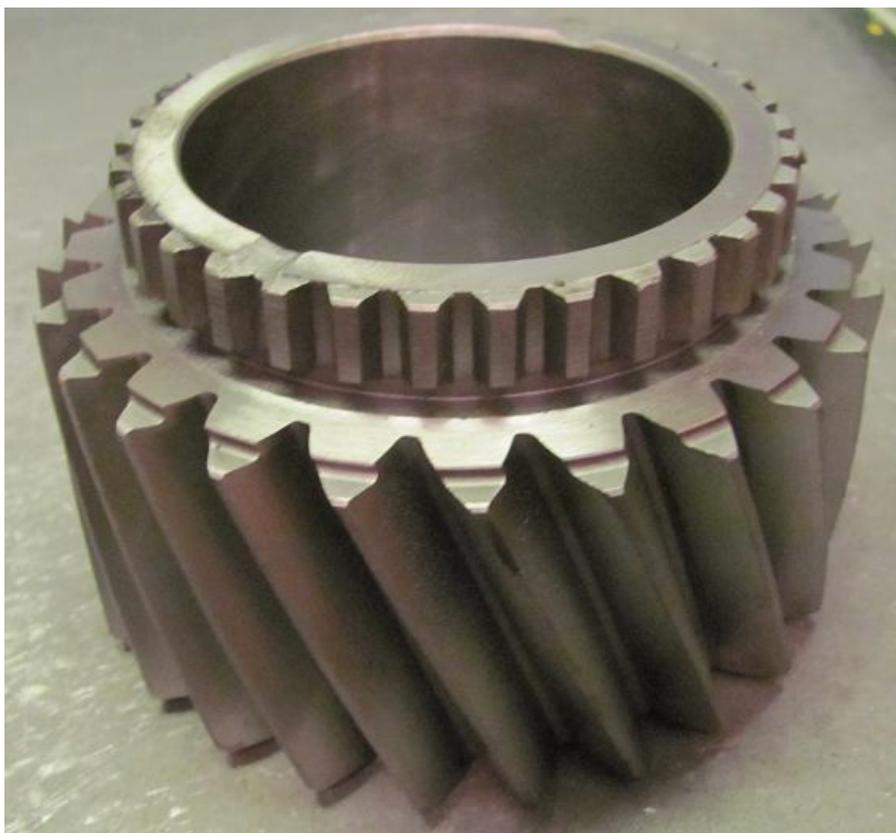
Шестерня 5-ой передачи вторичного вала 1509.1701132
